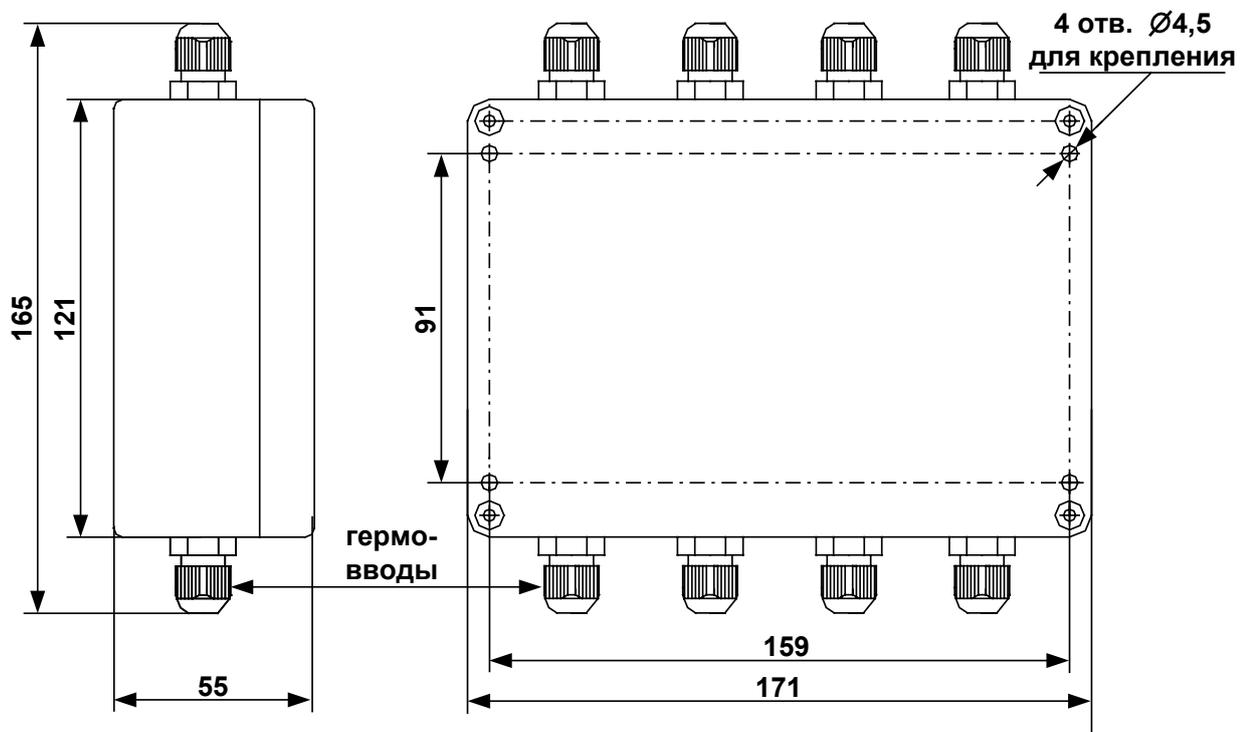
Внешний вид, габаритные и присоединительные размеры (исполнение IP65)
